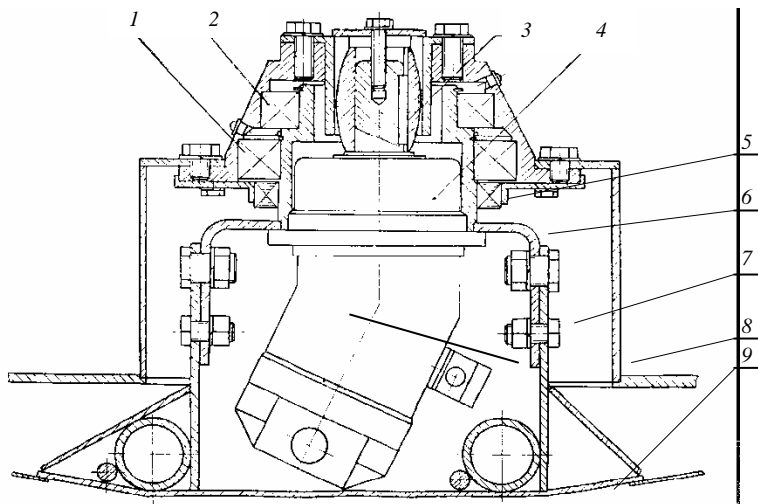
Привод двухроторного рабочего органа: 1, 2 – подшипники; 3 – гидромотор; 4 – шлицевая втулка; 5 – уплотнение; 6 – стакан; 7 – болты; 8 – колпак; 9 – опора
